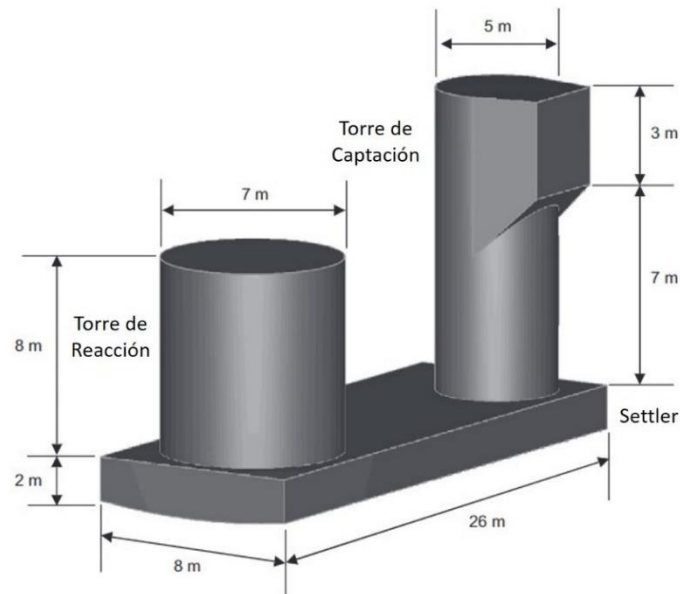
Dimensionamiento del Horno de fundición Flash. Fuente:(Schlesinger et al., 2011)
